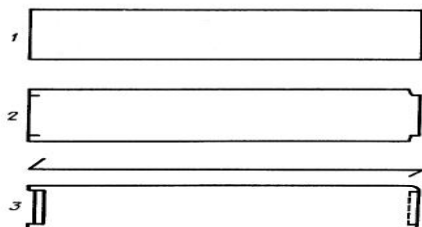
Последовательность обработки заготовки корпуса: 1 - заготовка; 2- обрубка углов и просечка; 3 - загиб полей
